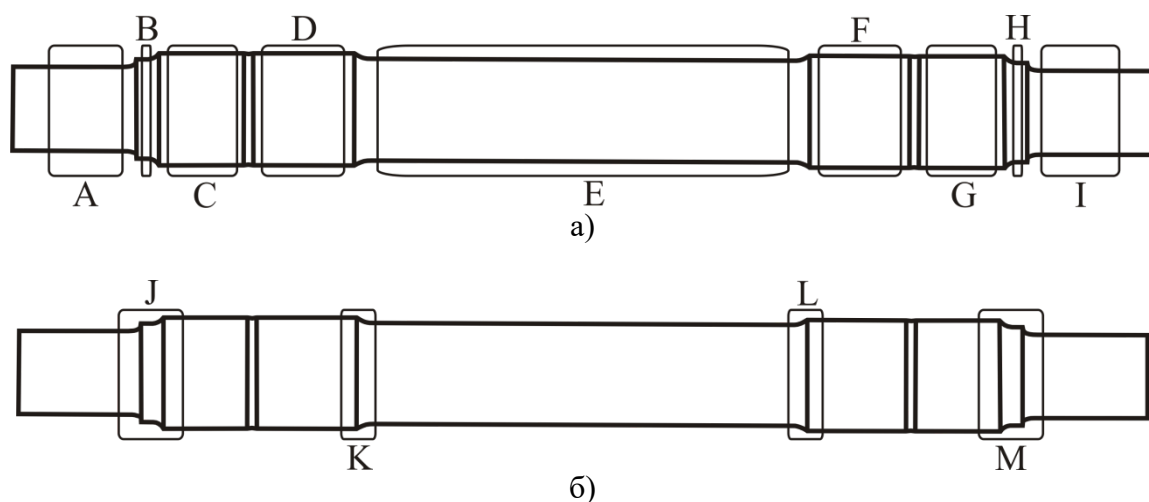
Зоны УЗК осей, подвергаемые УЗК на стенде (а – по варианту метода А2; б – по варианту метода А3)
